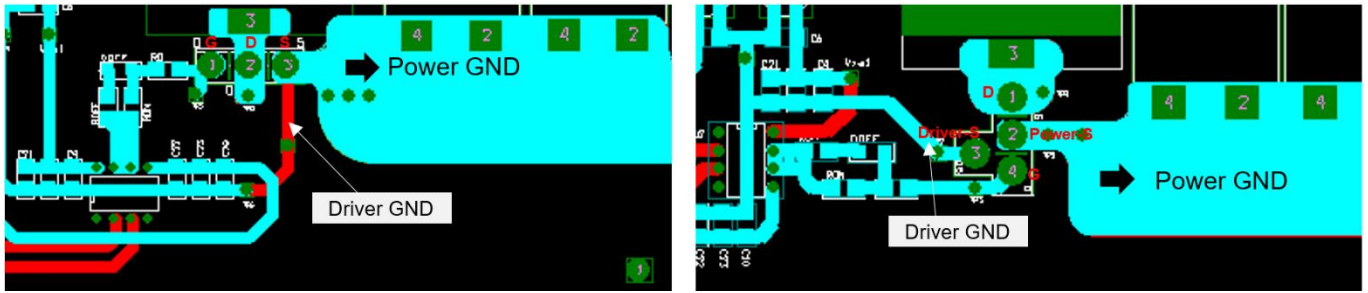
栅极驱动电路 PCB 布局: TO-247-3L (左) 与 TO-247-4L (右)
